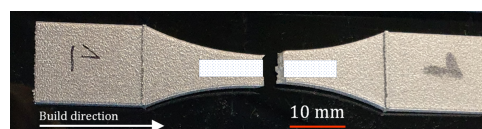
Ermüdungsprobe nach mechanischer Prüfung mit Markierung der gemessenen Fläche / Fatigue specimen after mechanical testing with measured area marking
